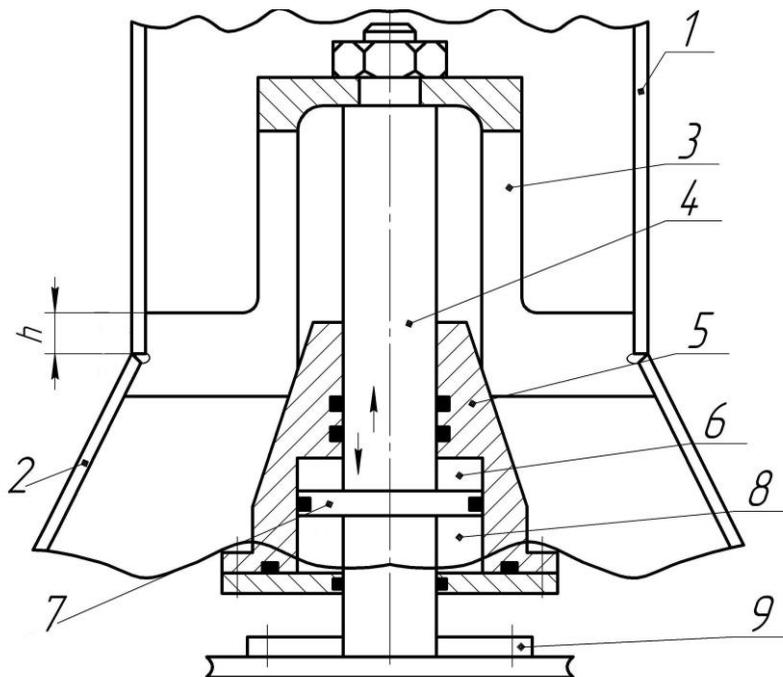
Конструктивная схема ССП для сборки и сварки соединения деталей 1 и 2
